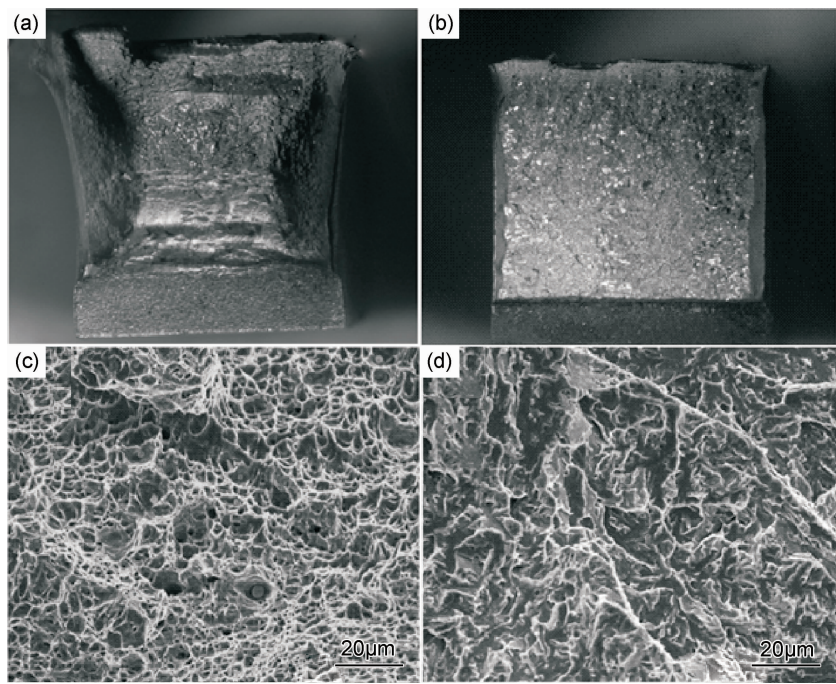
焊缝-40℃冲击断口形貌 (a)原始焊缝宏观形貌;
